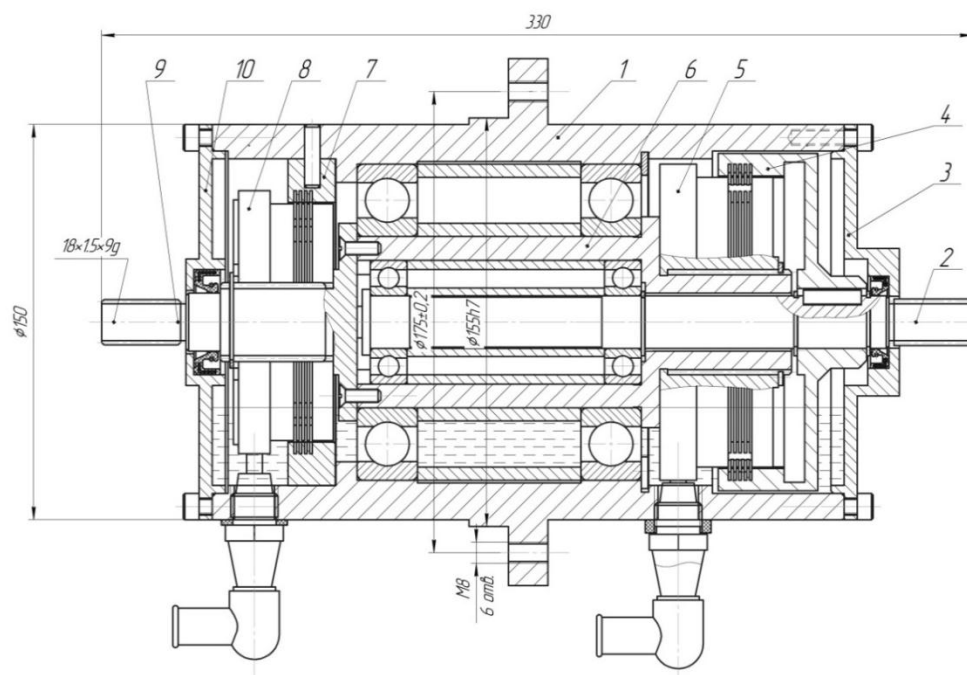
Муфта сцепления-торможения: 1 – корпус; 2 – входной вал; 3 – крышка входного вала; 4 – стакан; 5 – муфта ЭТМ-092; 6 – шлицевый вал; 7 – тормозное кольцо; 8 – муфта ЭТМ-072; 9 – выходной вал; 10 – крышка выходного вала
